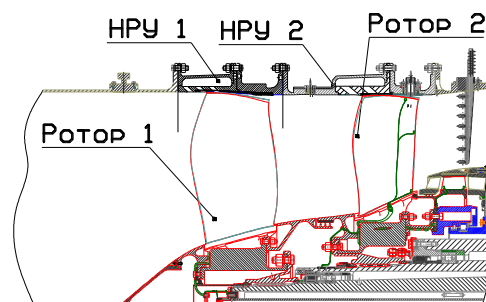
Продольный разрез модели вентилятора CRTF2a с корпусами
